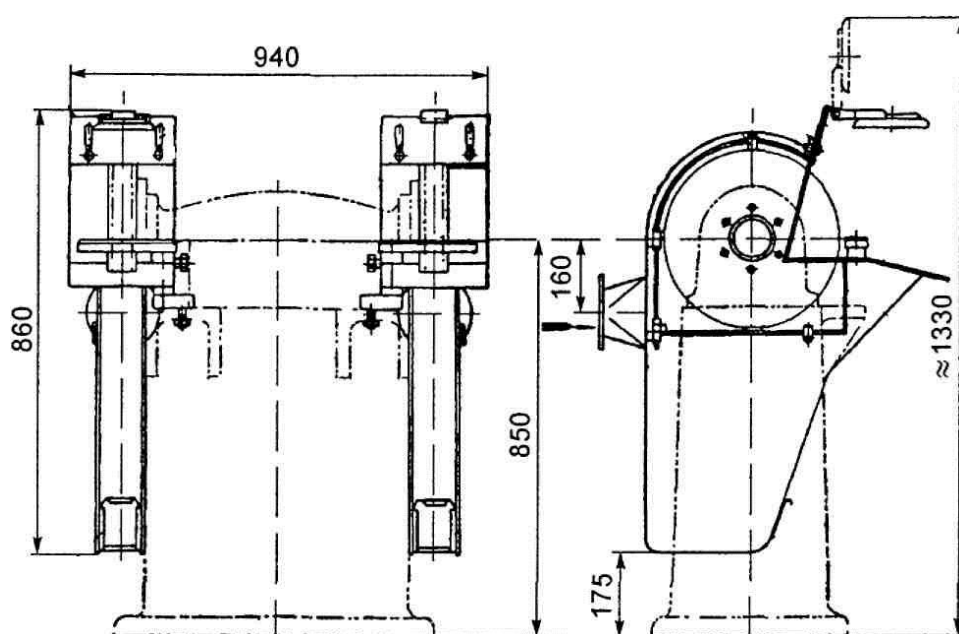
Кожухи обдирочно-шлифовального станка
